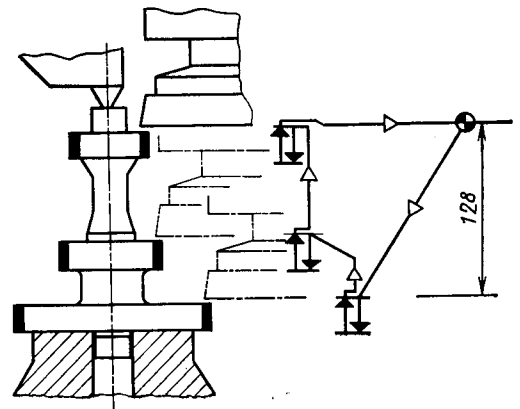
Схема долбления заготовки зубчатого колеса за один установ
